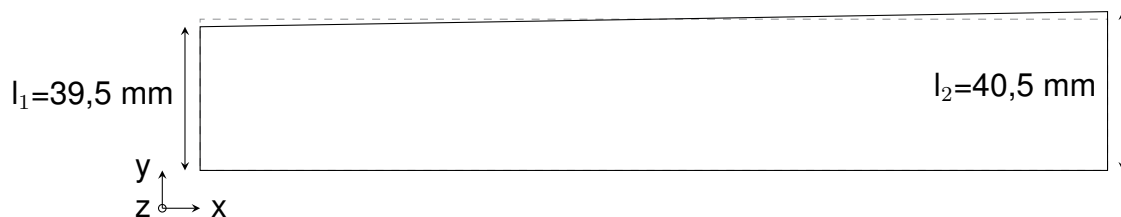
Section trapézoïdale dans le plan (xy)
